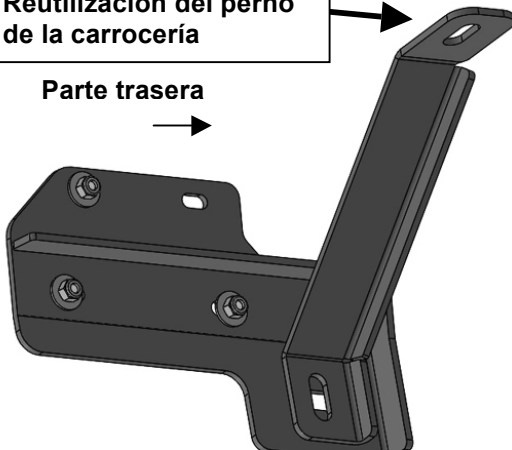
Instalación de soporte de montaje trasero del lado del pasajero
